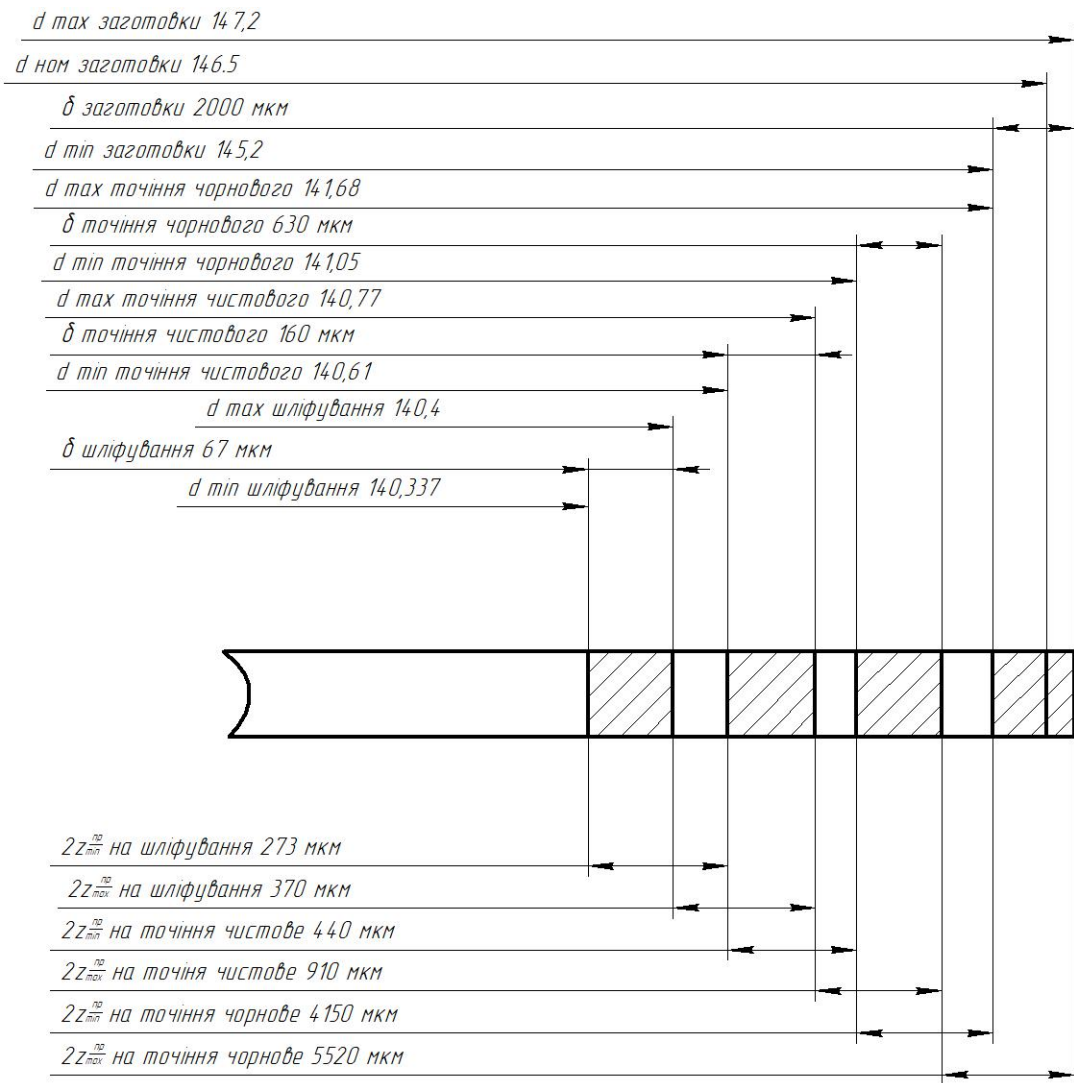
Схема графічного розташування припусків та допусків
